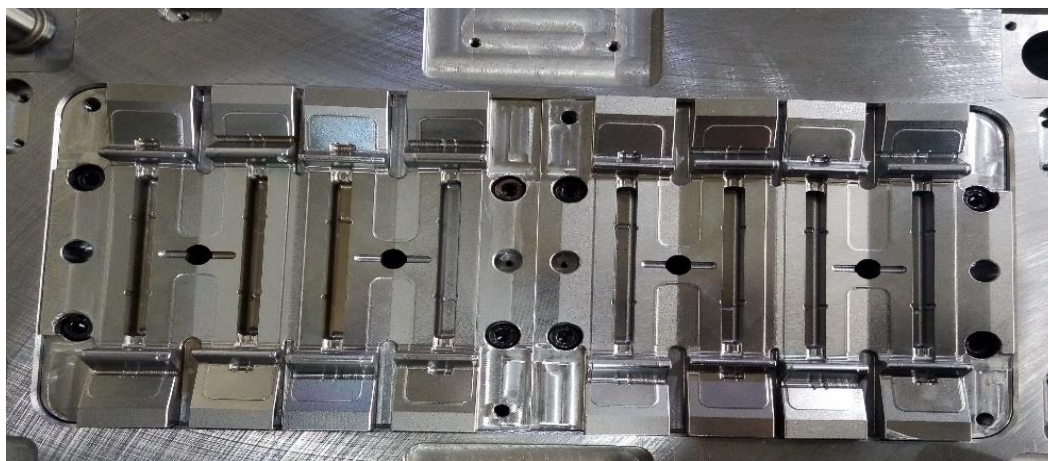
Molde Estruturado (Standarmoldes, 2019)
